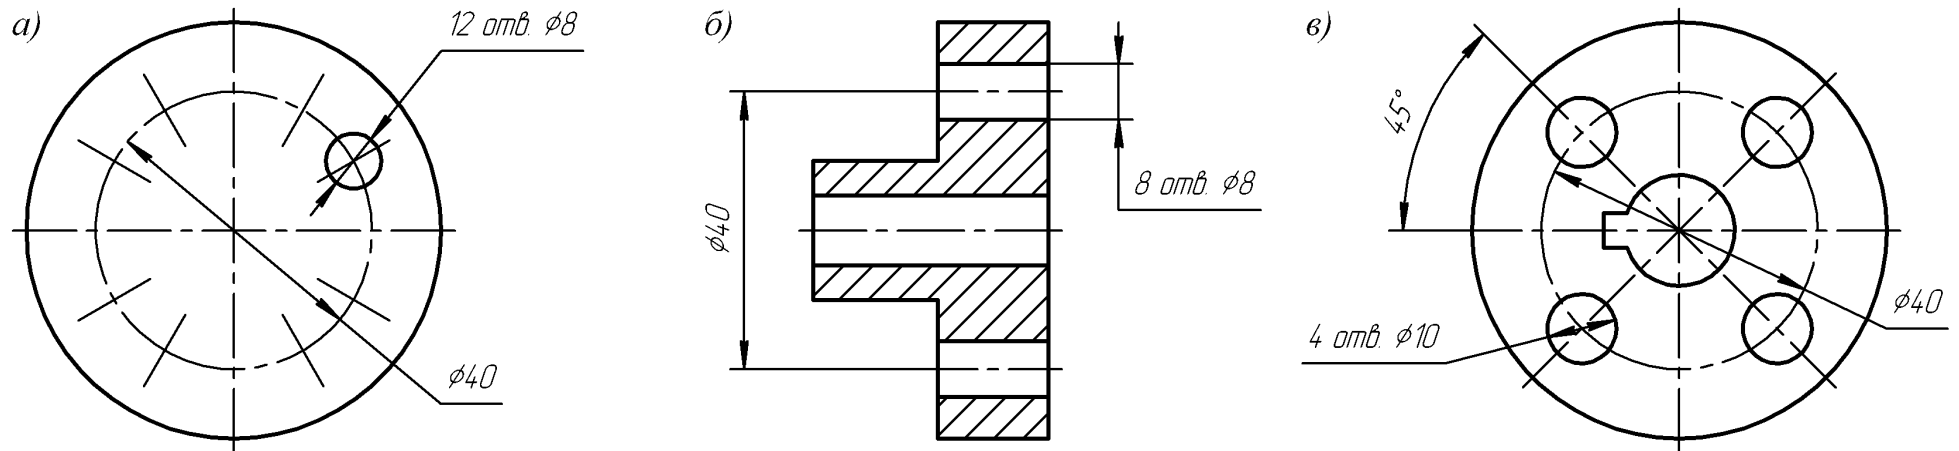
Простановка размеров отверстий, расположенных равномерно по окружности
